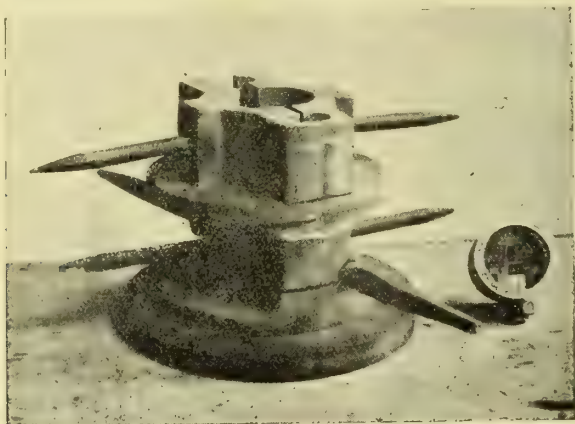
Piston de moteur (moule monté, pièce coulée vue du côté de la partie creuse).
